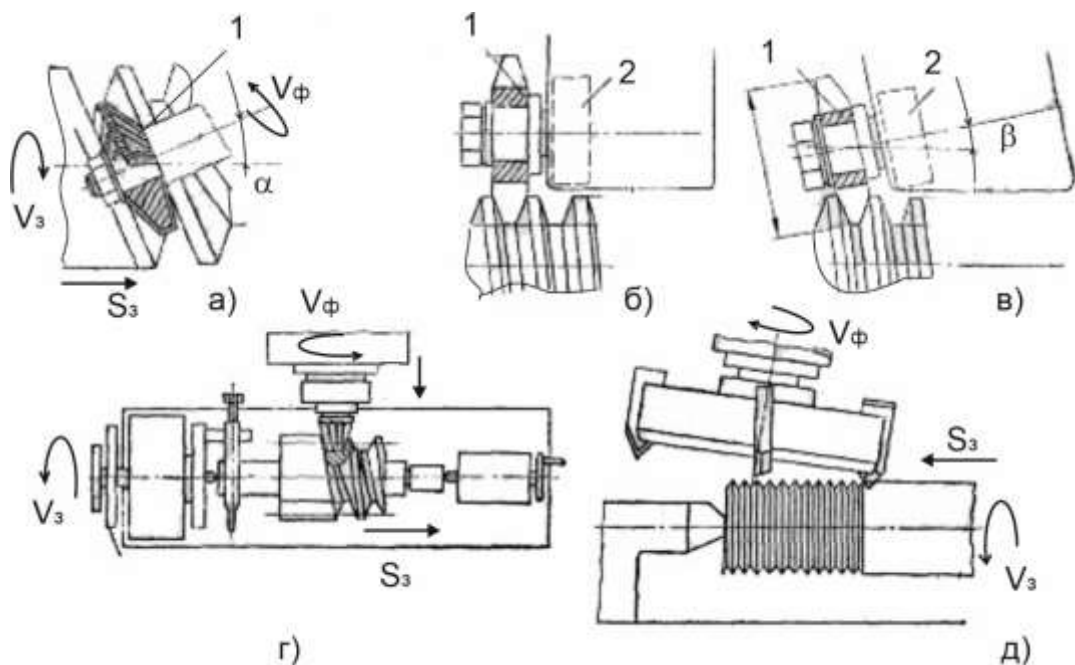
Схема фрезерування гвинтової поверхні:
